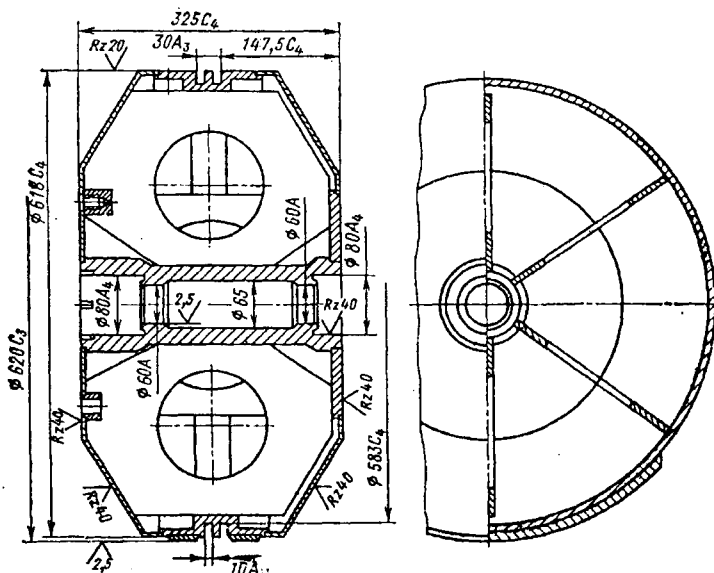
Поршень $\varnothing 620$ мм опозитного компресора 4М10-100/8.
